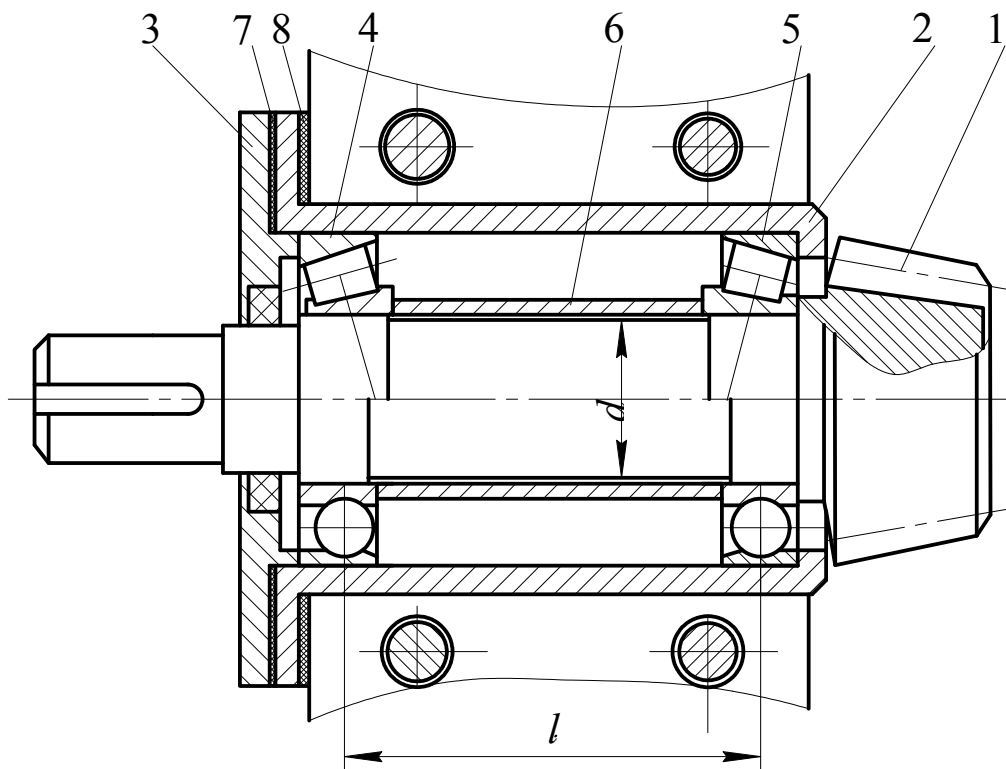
Конструкція підшипникового вузла конічної шестерні
